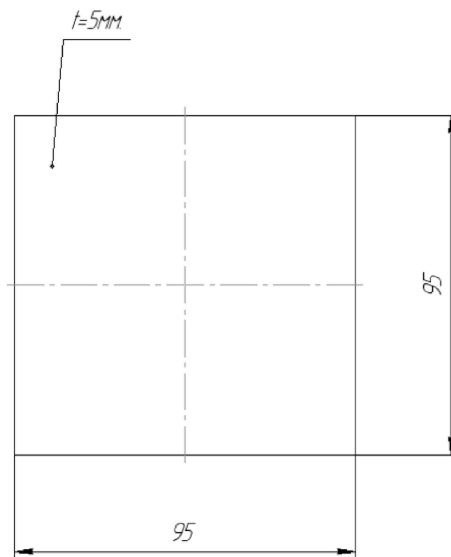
Ескіз заготовки для деталі «Пластина»
